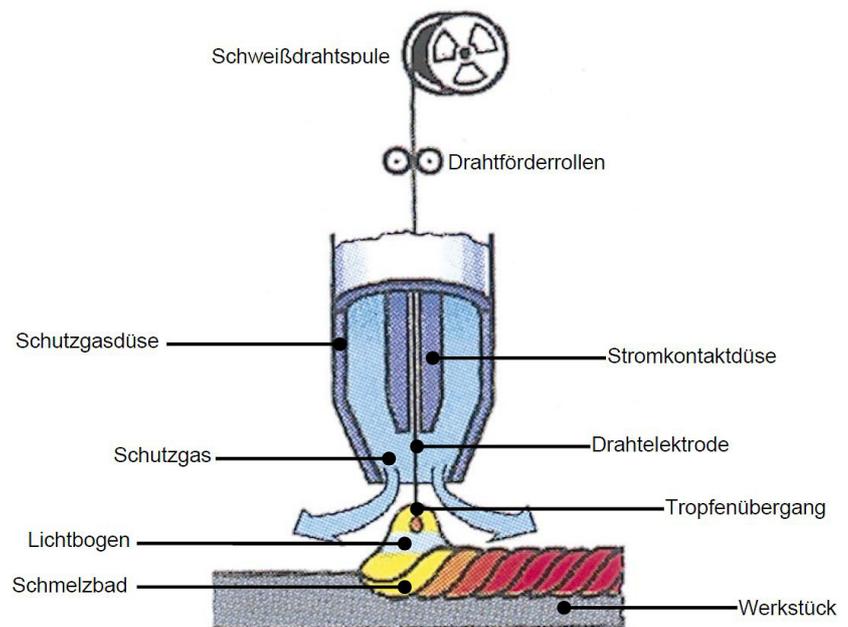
Funktionsprinzip Metall-Schutzgasschweißen
